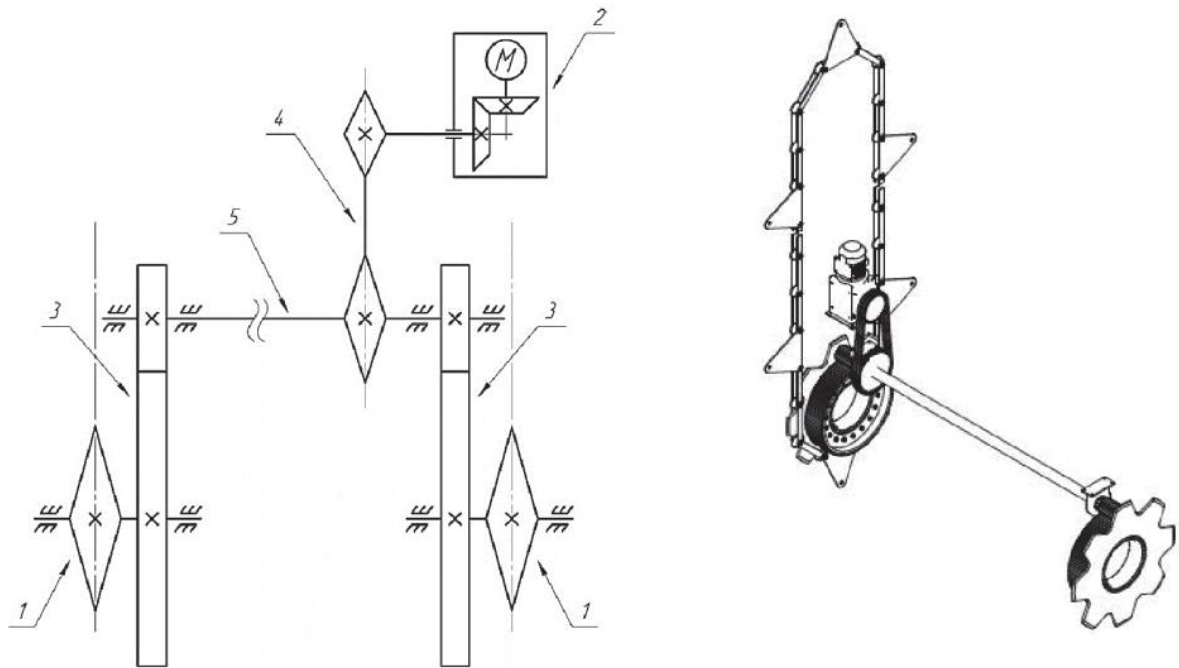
Кинематическая / реалистичная схема привода роторной автоматизированной парковки:
